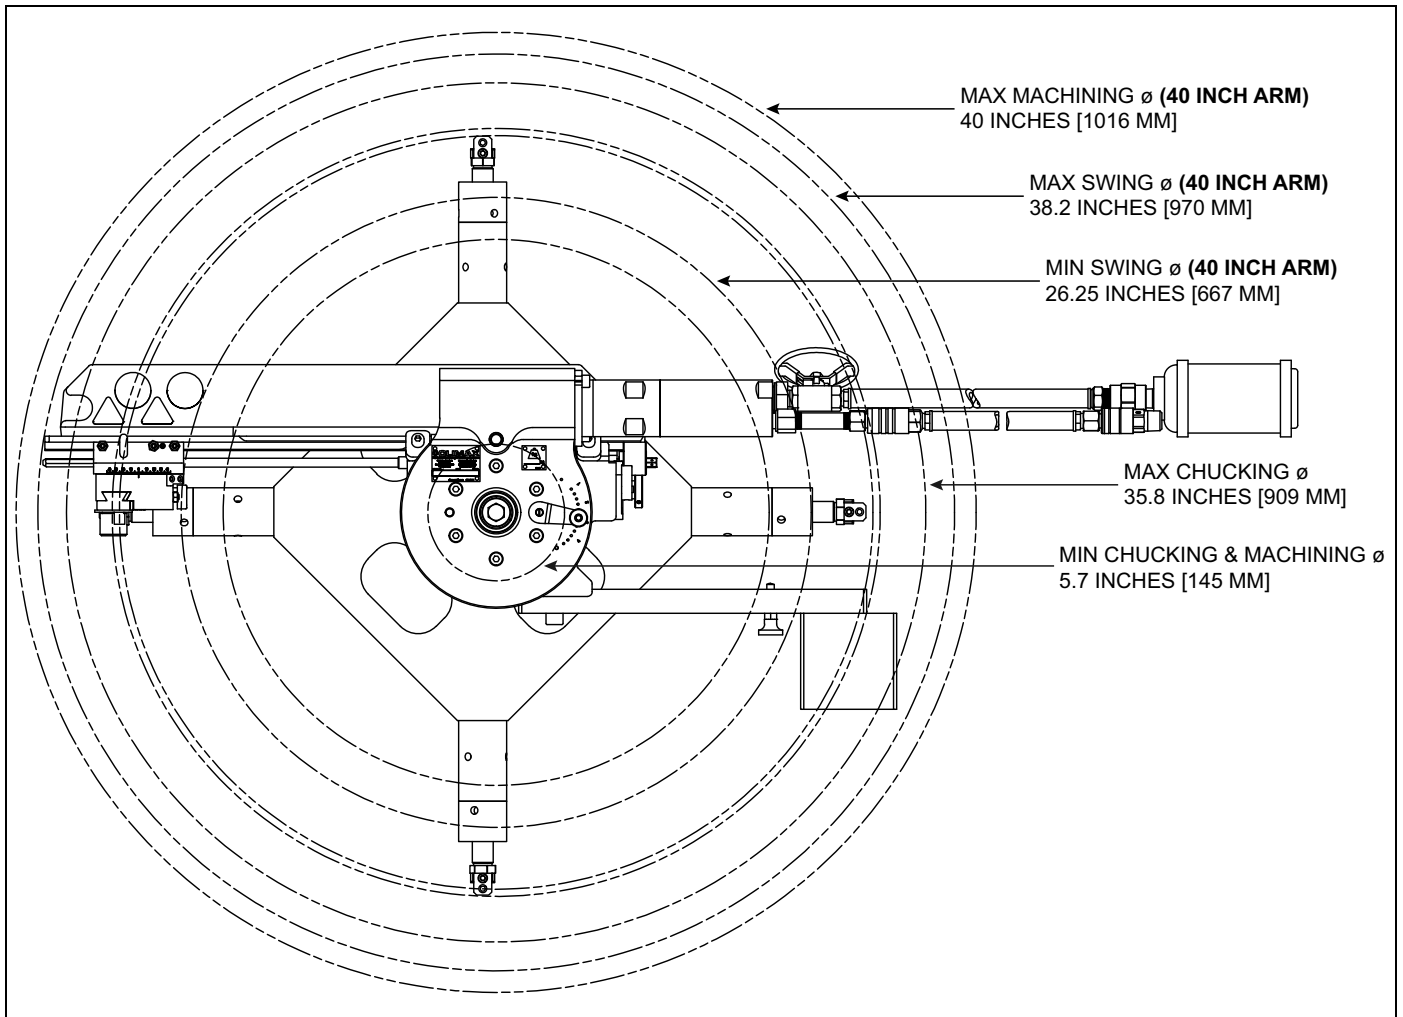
DIMENSIONS DU BRAS D'USINAGE 40" (1 016 MM)
